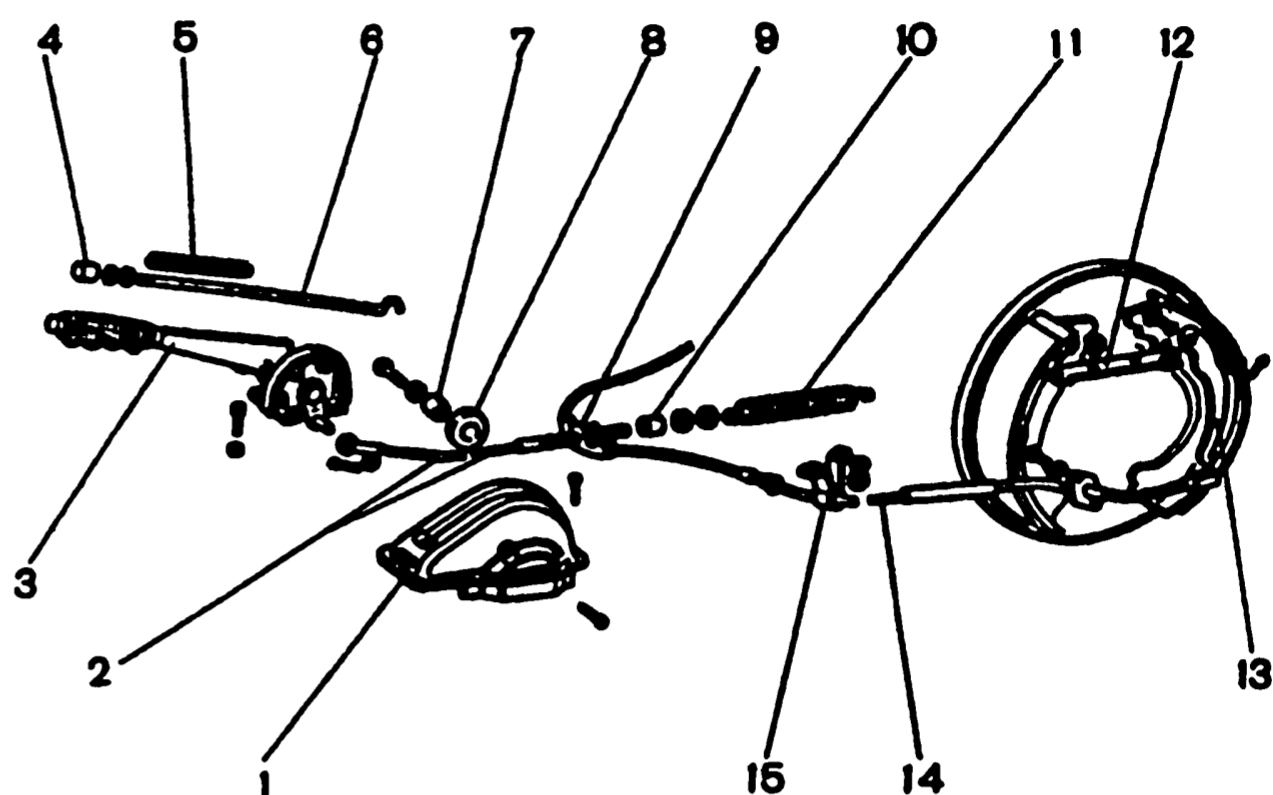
Детали привода стояночного тормоза: 1 - чехол; 2 - передний трос; 3 - рычаг; 4 - кнопка; 5 - пружина тяги; 6 - тяга собачки; 7 - втулка; 8 - ролик; 9 - направляющая заднего троса; 10 - распорная втулка; 11 - оттяжная пружина; 12 - распорная планка; 13 - рычаг ручного привода колодок; 14 - задний трос; 15 - кронштейн заднего троса
